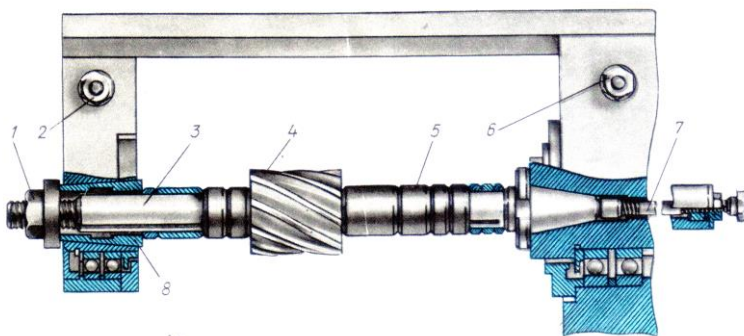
Схема установки цилиндрической фрезы на горизонтально-фрезерном станке: 1, 2, 6 – гайки; 3 – оправка; 4 – фреза; 5 – кольца; 7 – шомпол
